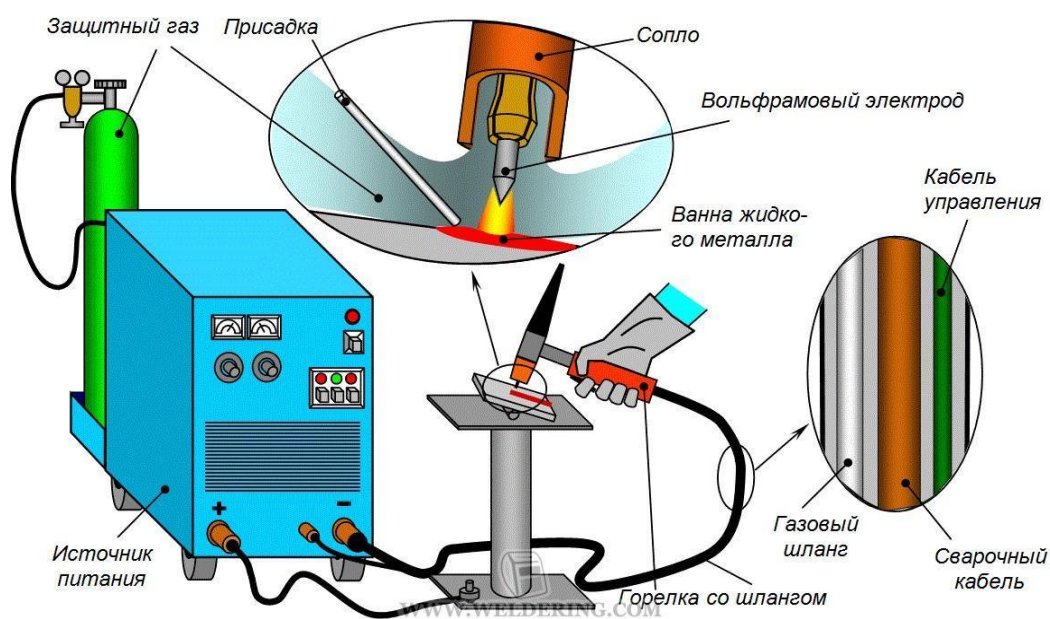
Схема участка для проведения сварки и ремонта деталей из алюминиевых сплавов
